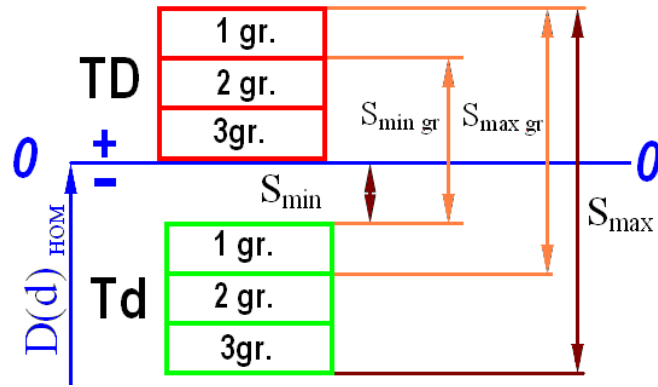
Схема сортування деталей за групами (посадка із зазором)
